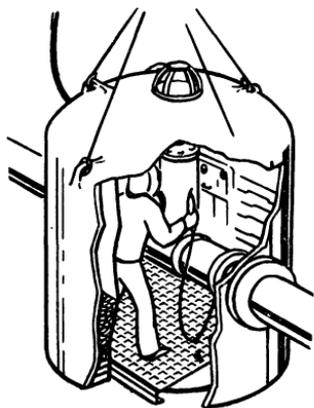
Пример выполнения подводной сухой сварочной камеры.
